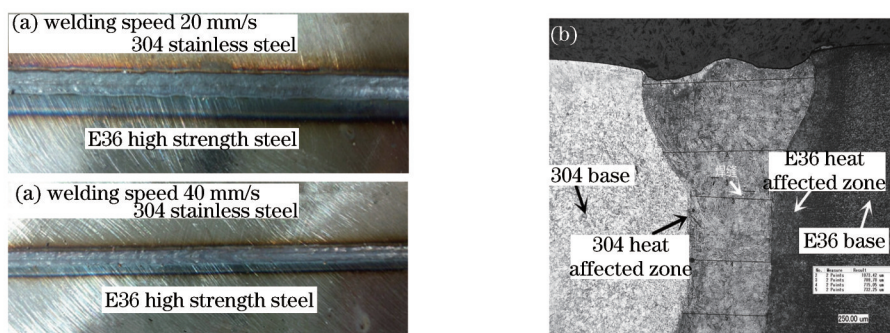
焊缝。(a)不同焊接速度焊缝形貌;(b)焊缝微观形貌
